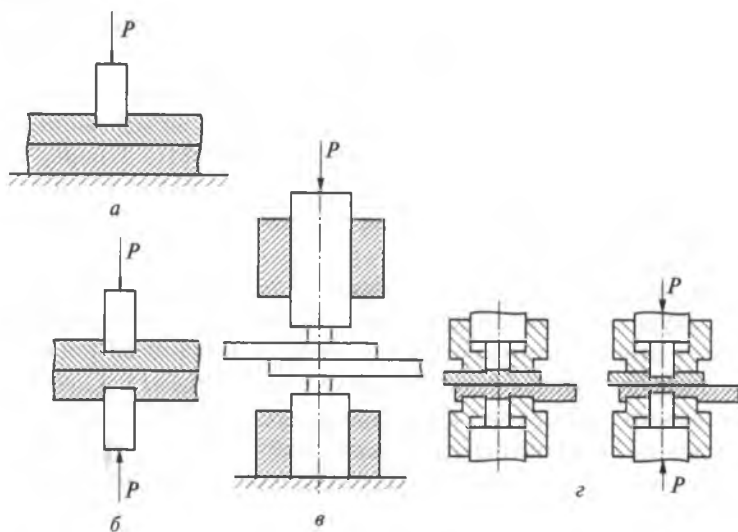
Схемы холодной сварки внахлестку:
